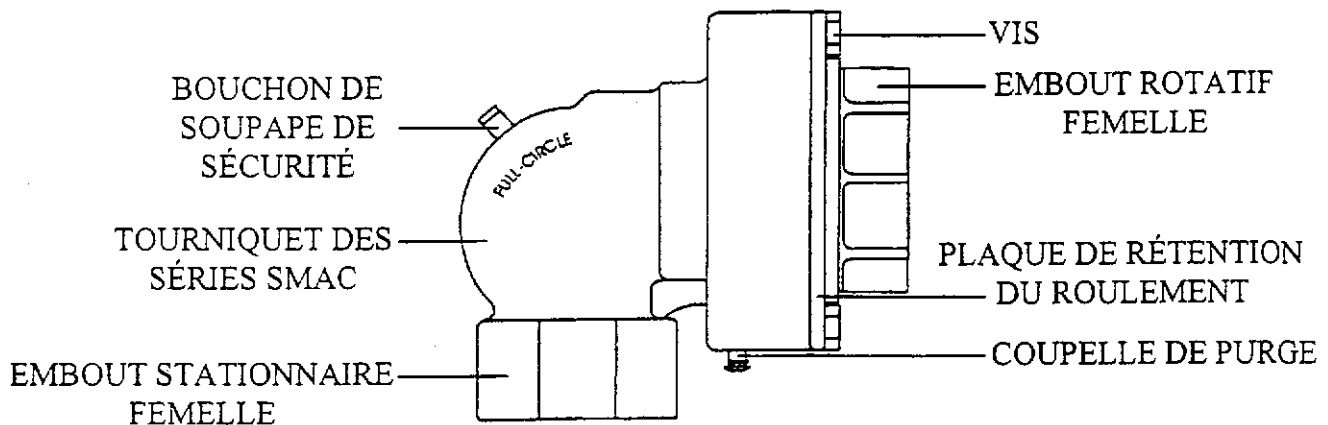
emplacement de la coupelle de purge - INSTALLATION POUR ENROULEUR DE TUYAU
